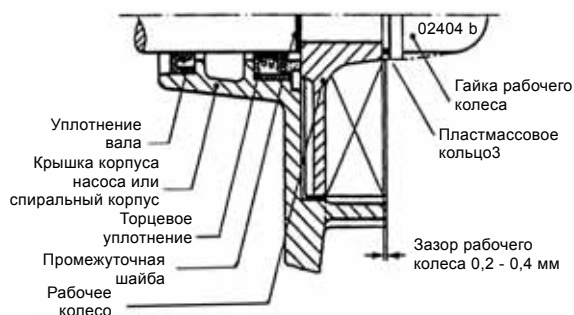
Сборка рабочего колеса POMONA 23, 32, 42
